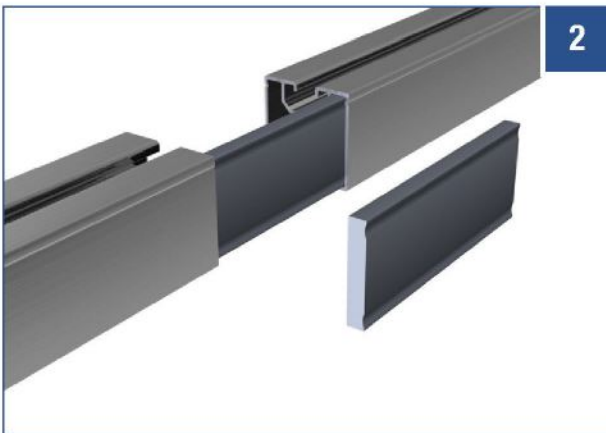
La pieza de unión (PROFINESS 18) se inserta hasta la mitad en el carril de montaje. A continuación, deslizar el otro carril de montaje sobre la pieza de unión. Por último, empalmar completamente hasta hacer tope presionando los carriles de montaje entre sí.
